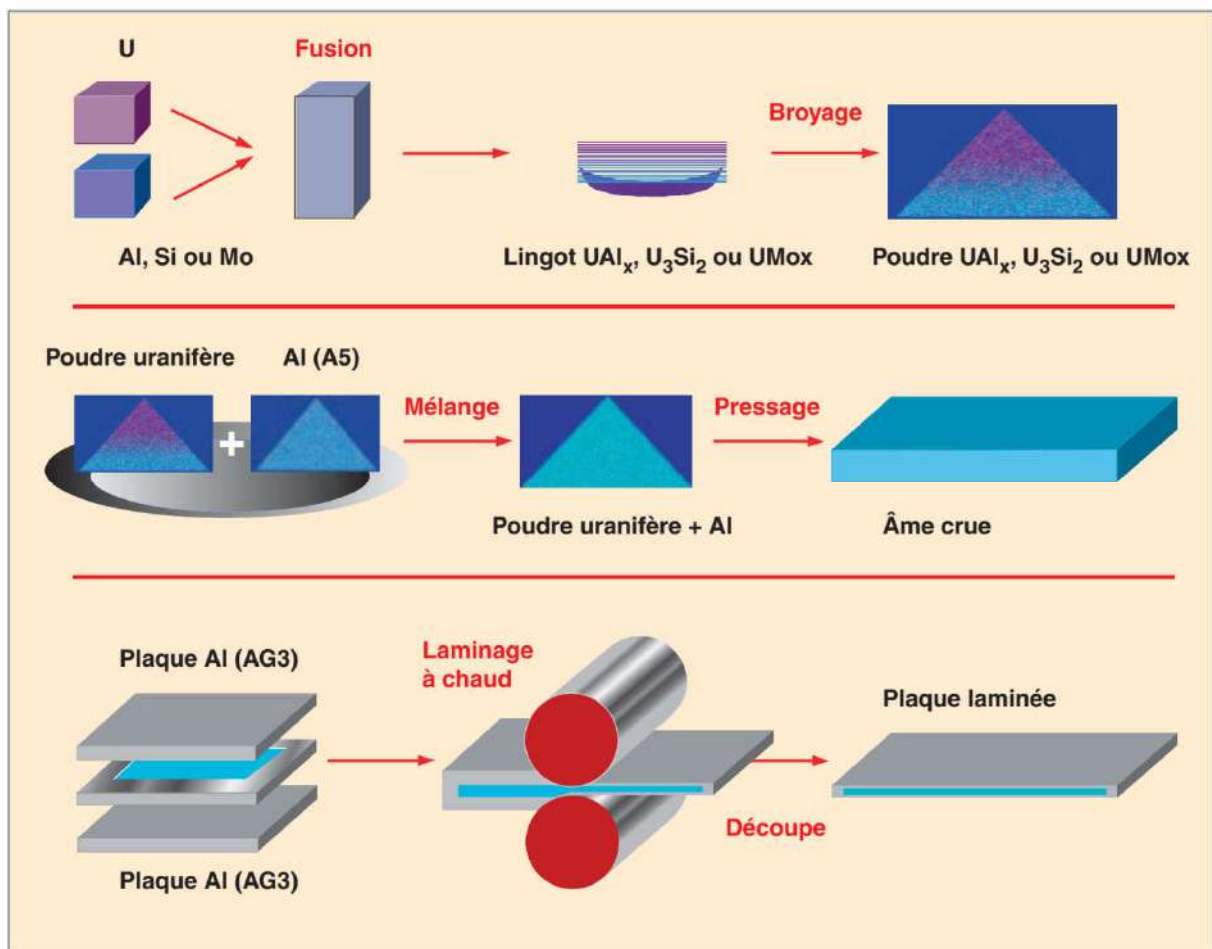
Principe du procédé de fabrication de plaques combustibles par « colaminage ».
